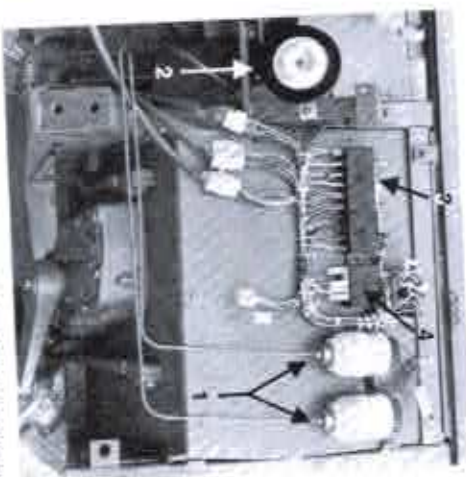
ab Chassis Nr. 19111 Typ 1800 ab Chassis Nr. 18504 Typ 1800
